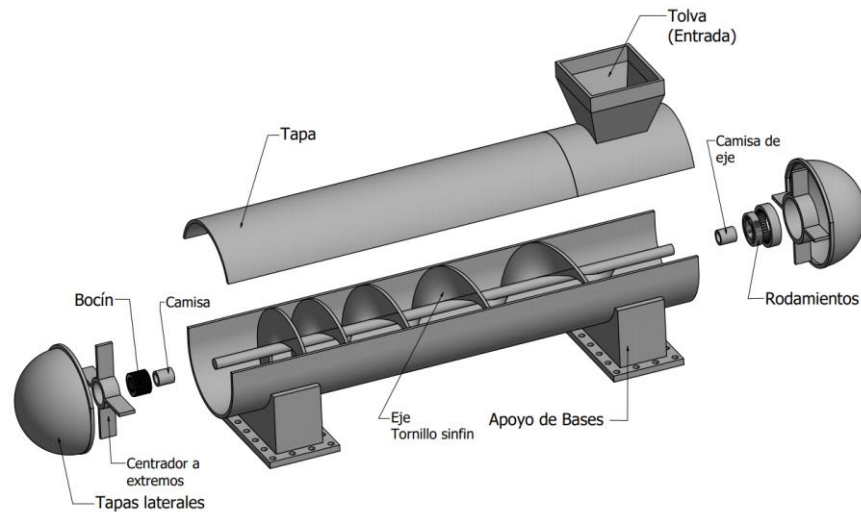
Despiece de un sistema transportador de tornillo sin fin
